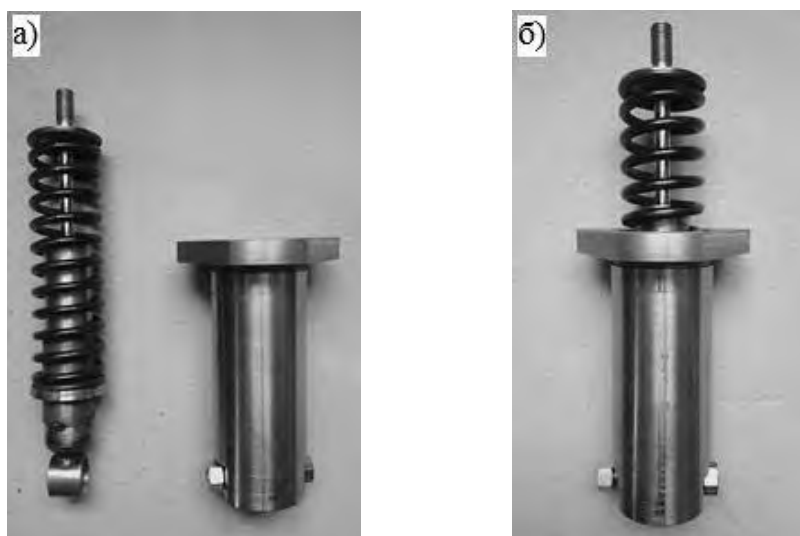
Внешний вид одной стойки опытной подвески кабины колесного трактора: а – опытный демпфер в сборе и кронштейн; б – стойка в сборе
